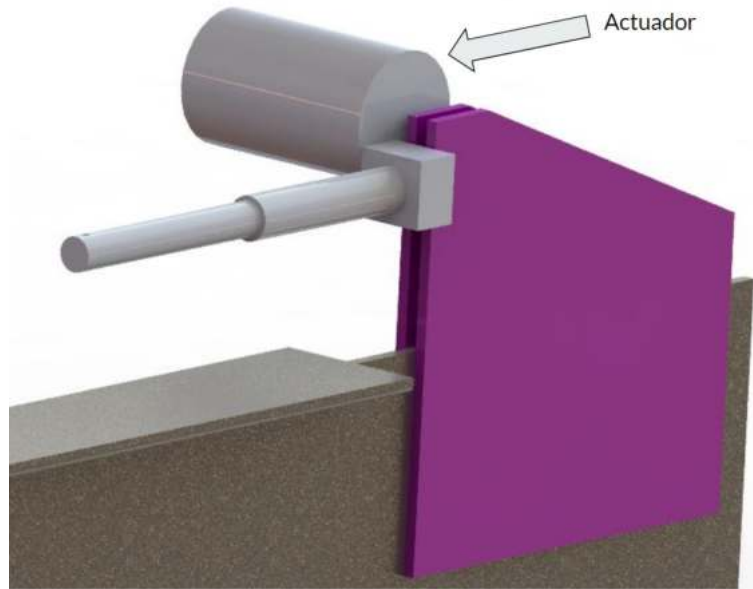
Prototipo de anclaje de motor con chapas soldadas al alma del perfil.
